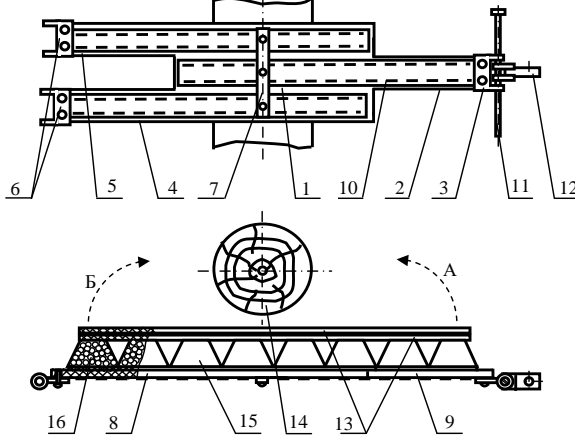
Адаптивна самозатискна петля-захват тросового струшувача: А, Б – напрями охоплення штамба рукавами; 1 – еластична основа; 2 – правобічний рукав; 3 – шарнір правобічного рукава; 4 – нижня гілка лівобічного рукава, 5 – верхня гілка лівобічного рукава; 6 – шарніри лівобічних рукавів; 7 – пластина; 8 – прогумований пас лівобічних рукавів; 9 – прогумований пас правобічного рукава; 10 – скоби; 11 – палець; 12 – кронштейн, 13 – еластичні стрічки; 14 – штамп дерева; 15 – оболонка; 16 – сипкий наповнювач
